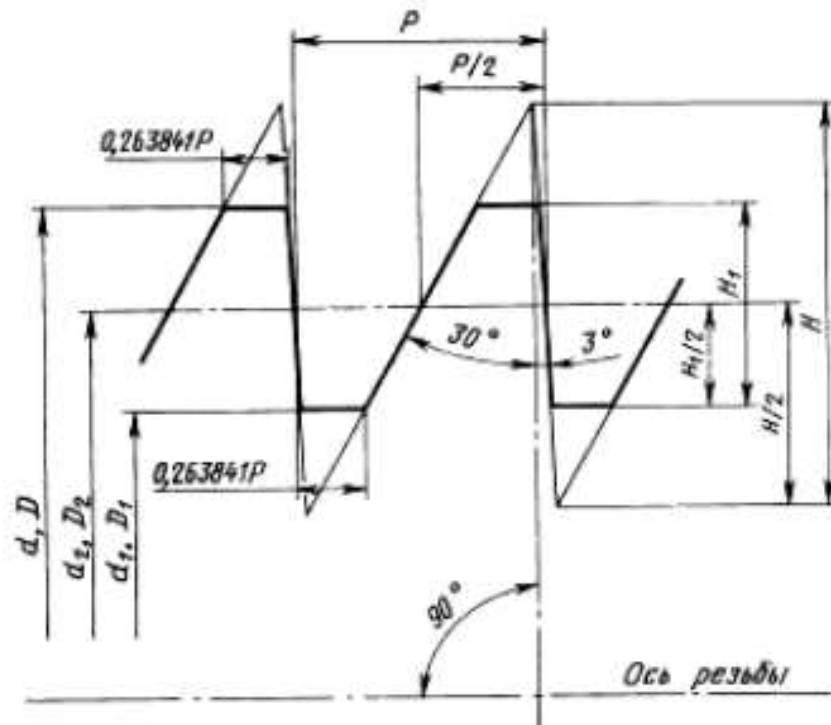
Профиль резьбы по ГОСТ 10177-82
